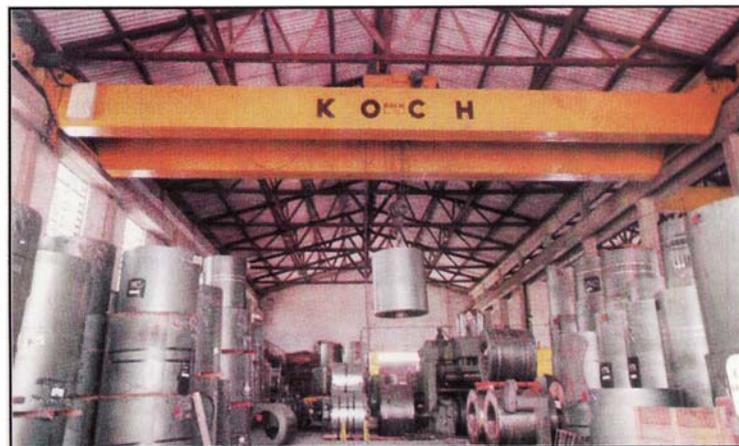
Ponte rolante de viga movimenta bobinas metálicas.
